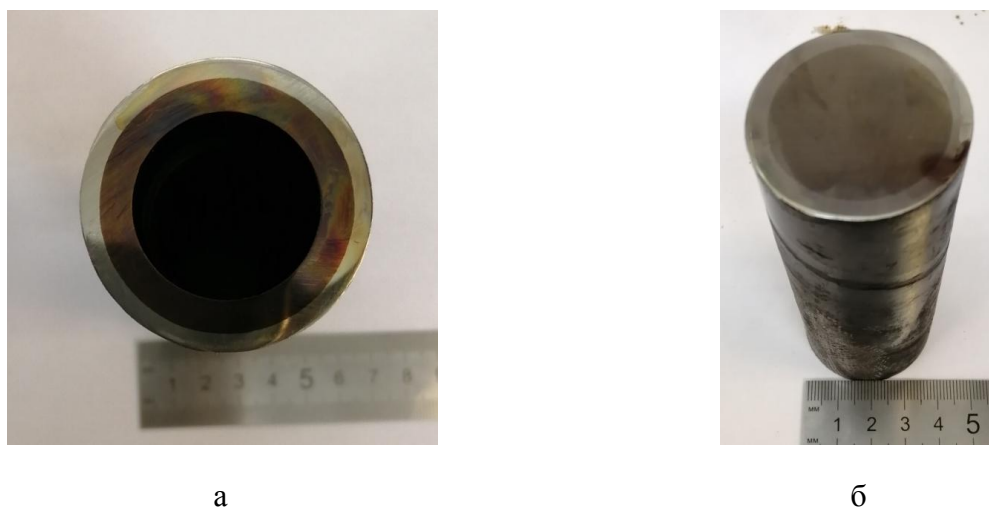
Цилиндрические заготовки после сварки взрывом и прокатки (наружный слой сталь 08X18H10T, внутренний сталь 20): а – биметаллическая труба; б – биметаллический стержень.
